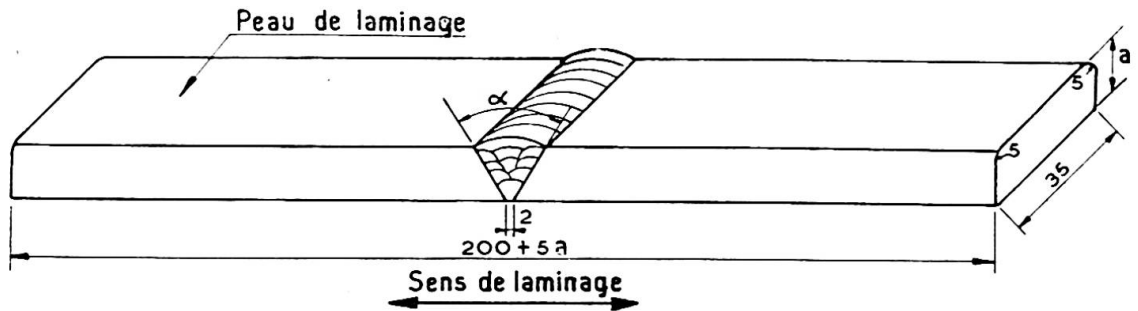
Forme et dimensions de l'éprouvette de l'essai de pliage d'un joint soudé.
